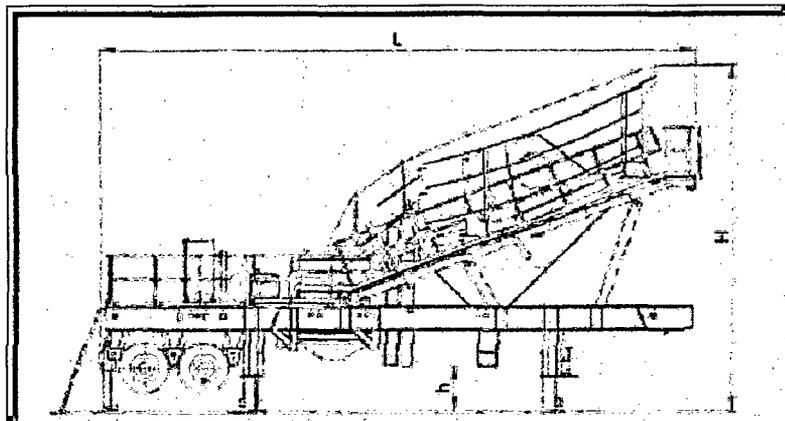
Vista del montaje de operación de la planta trituradora portátil según fabricante
